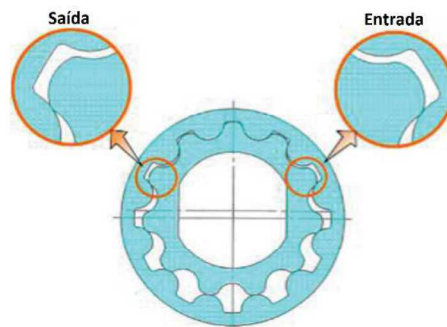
Contacto entre engrenagens e corpo. Adaptado de [15].
